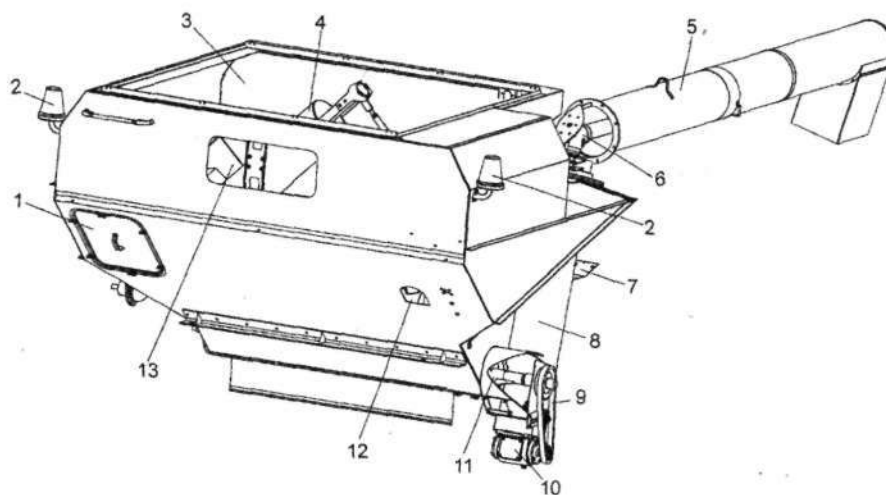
Бункер зерновой: 1 – крышка лаза в бункер; 2 – маяки проблесковые; 3 – бункер; 4 – шнек загрузной; 5 – шнек поворотный выгрузной; 6 – отвод с редуктором; 7 – настил; 8 – шнек наклонный выгрузной; 9 – ременная передача привода шнека горизонтального; 10 – редуктор; 11 – шнек горизонтальный; 12 – окно пробоотборника; 13 – смотровое окно
